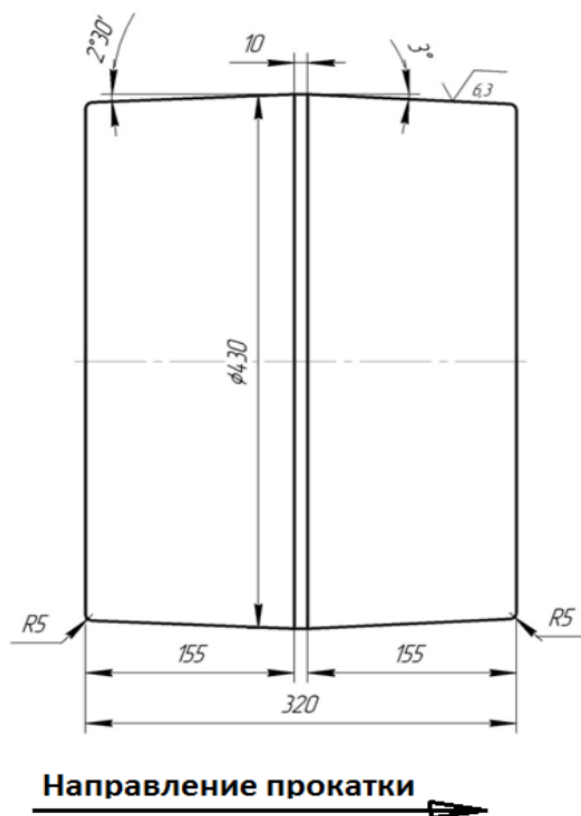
Бочковидный валок стана винтовой прокатки МИСиС-130Д
